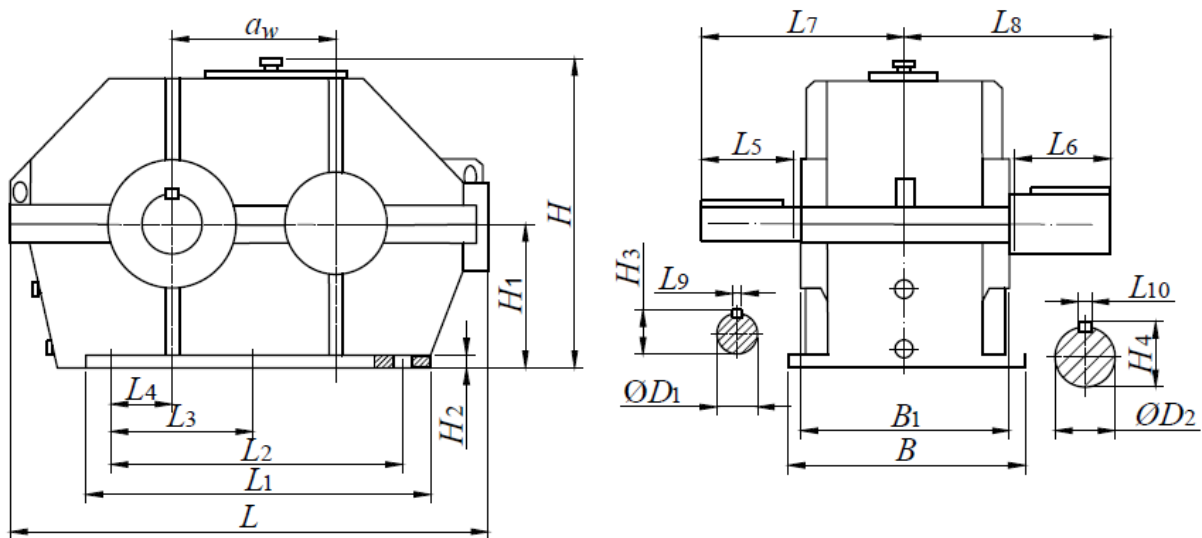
Редуктор цилиндрический одноступенчатый типа Ц
